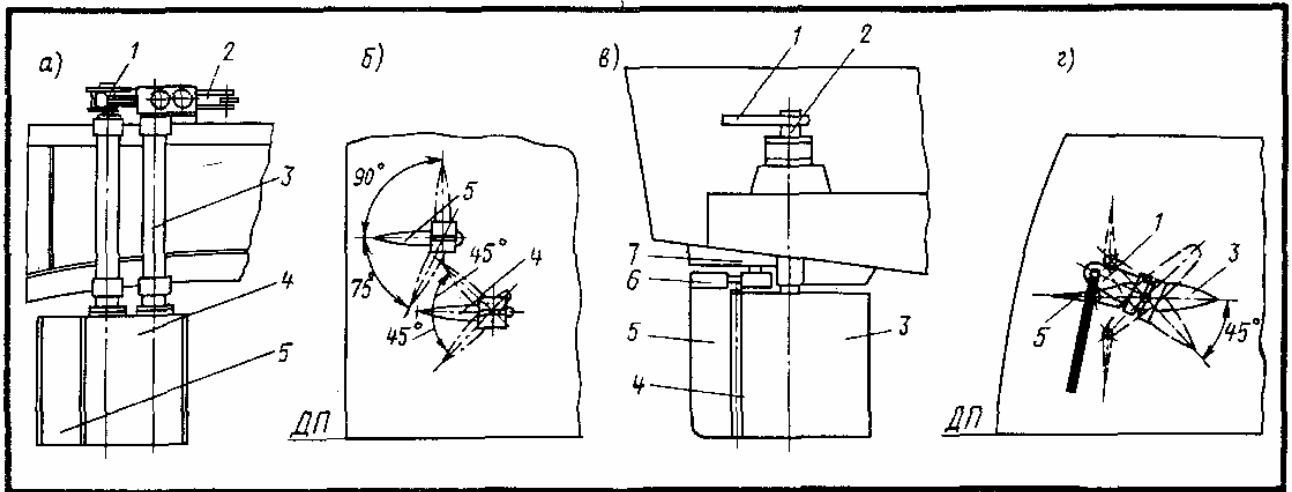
Схемы рулевых устройств : а – с рулями Енкеля (вид сбоку); б – то же (вид сверху).
